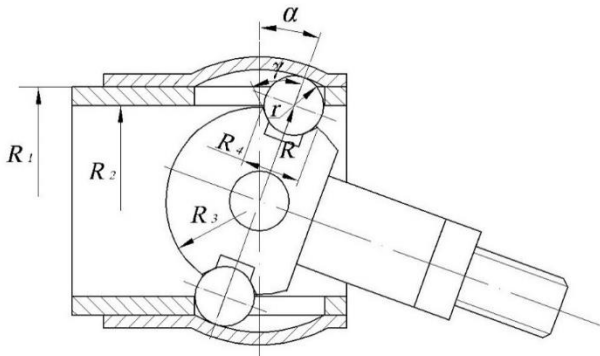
Розрахункова схема конструкції шарнірного з'єднання гвинтового робочого органу.
